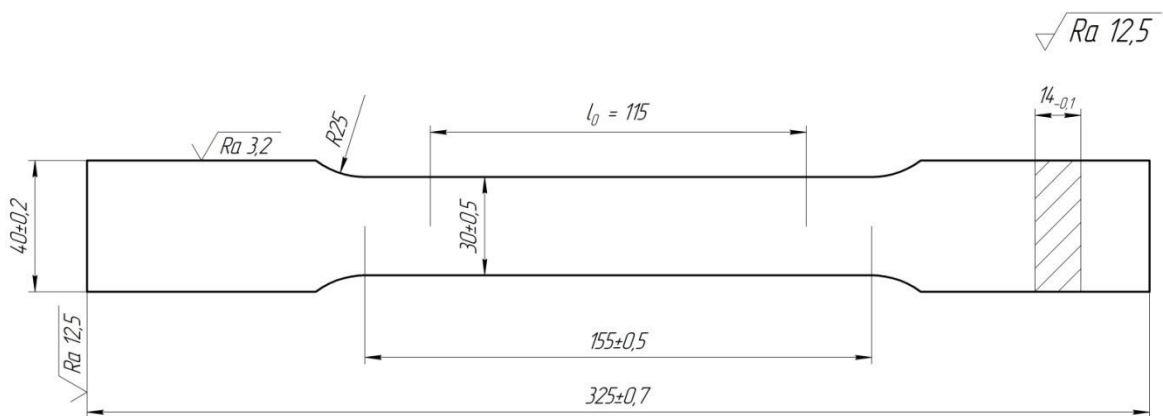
Чертеж и вид образцов для прочностных испытаний
